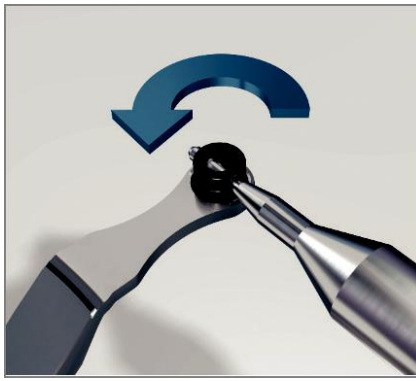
Montage (serrage) du raccord de guide de fraisage sur le manche du guide de fraisage
